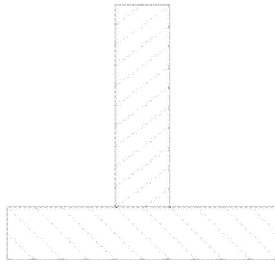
Bezeichnung Schweißzusatz
